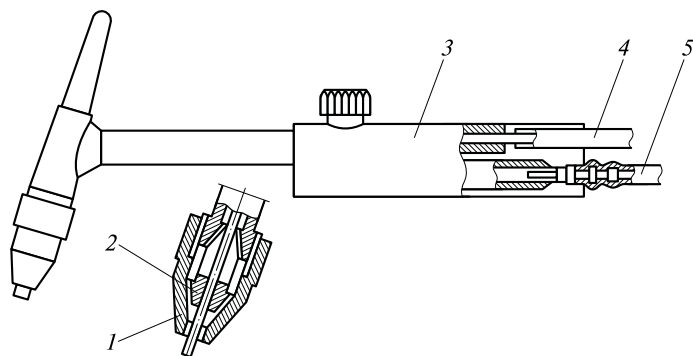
Горелка для ручной дуговой сварки в защитном газе:
